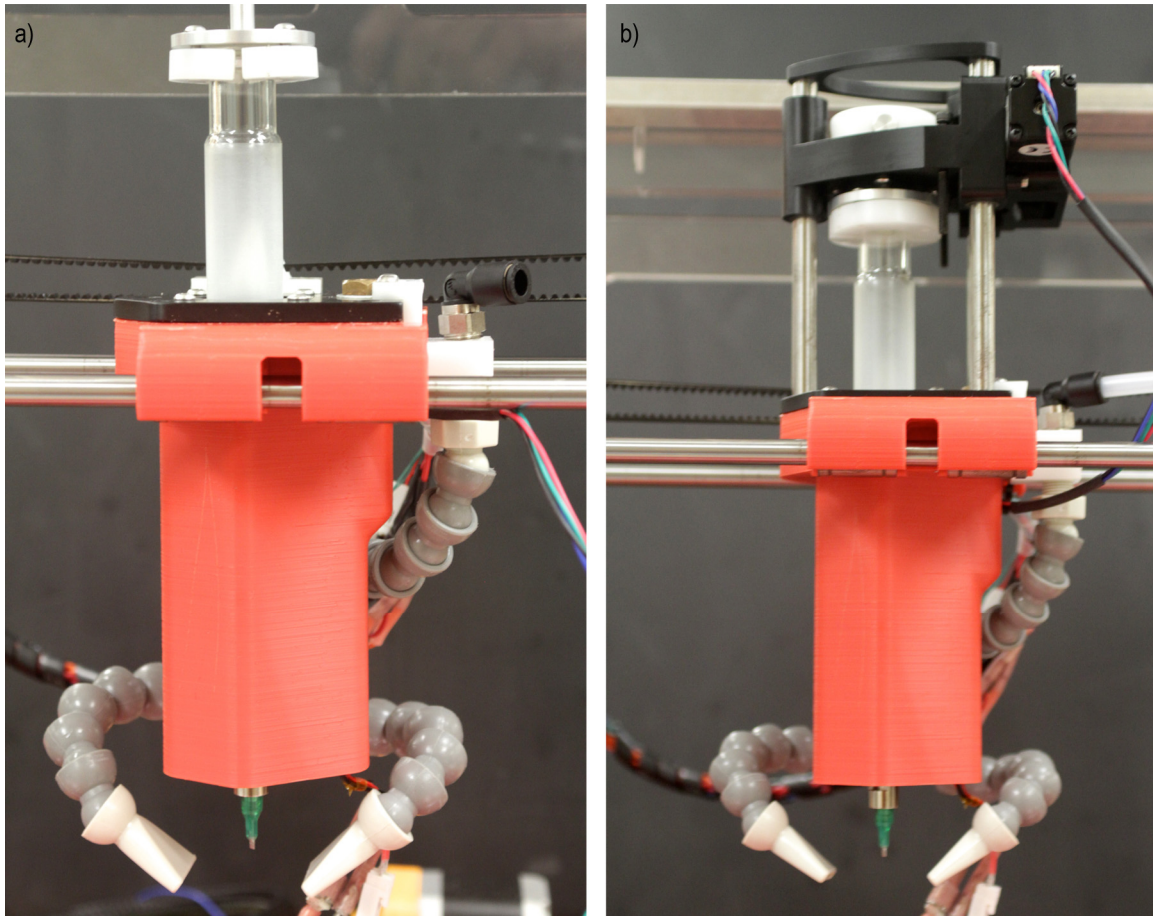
Photos de la tête d'impression pendant son assemblage. a) Le sous-assemblage de la seringue a été placé dans le support et le système de refroidissement a été vissé au couvercle. b) Les guides, le chariot et le support des guides ont été remis en place et la butée du piston a été vissée dans la rotule.
